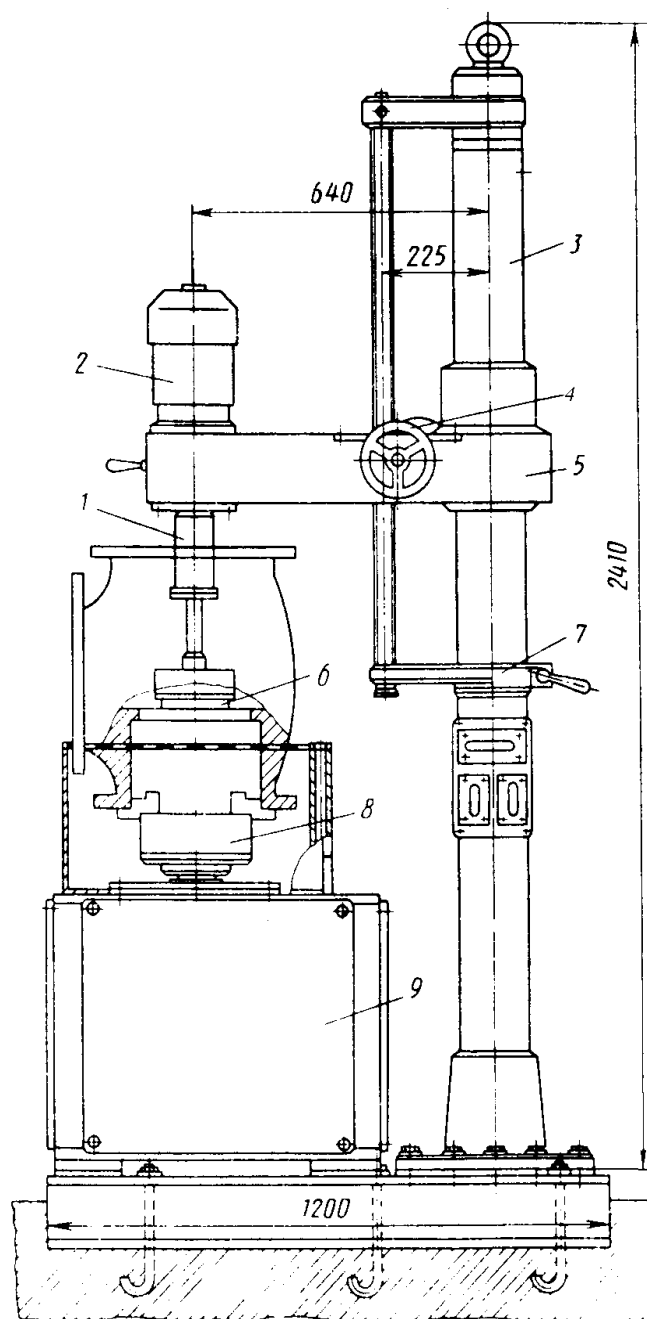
Станок для шлифовки уплотнительных поверхностей арматуры до D_y 600 мм.
